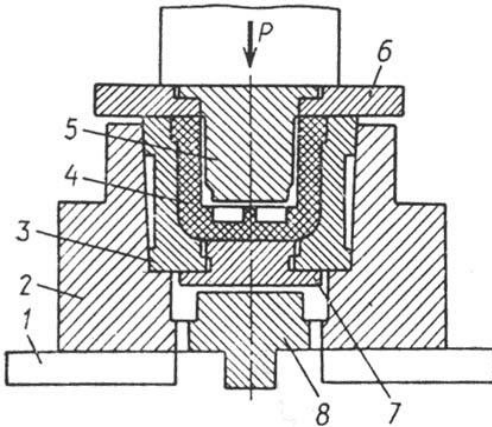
Відновлення деталей насоса типу НШ-У обтисканням: 1 – станина преса; 2 – пресформа; 3 - блок матриць; 4 - корпус насоса; 5 - пуансон; 6 - плита; 7- кільце; 8 – виштовхувач
